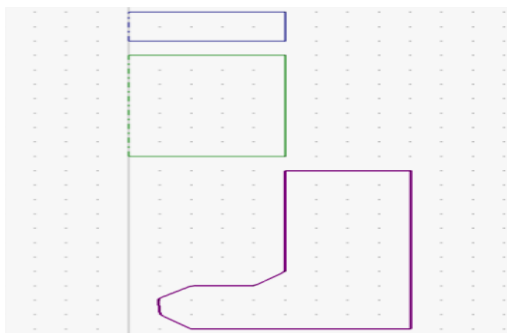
Верхний инструмент, заготовка и нижний инструмент, модуль QDraft программы QForm
